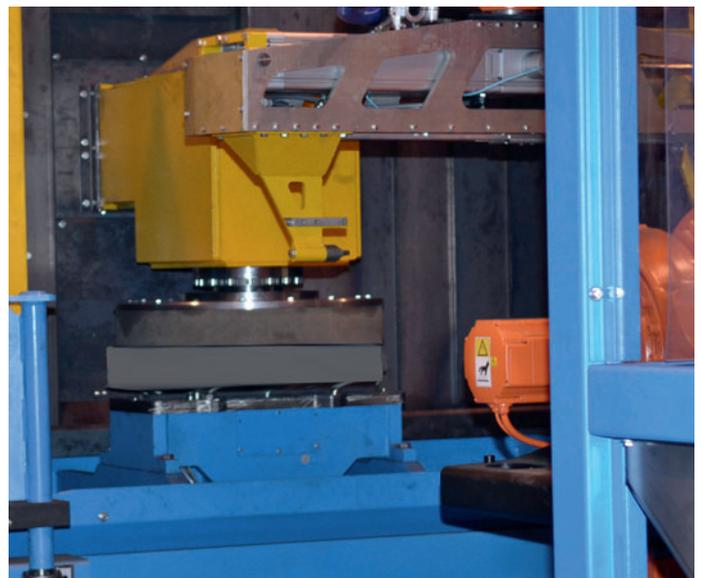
Schleifmaschine mit Bauteil in Bearbeitung
